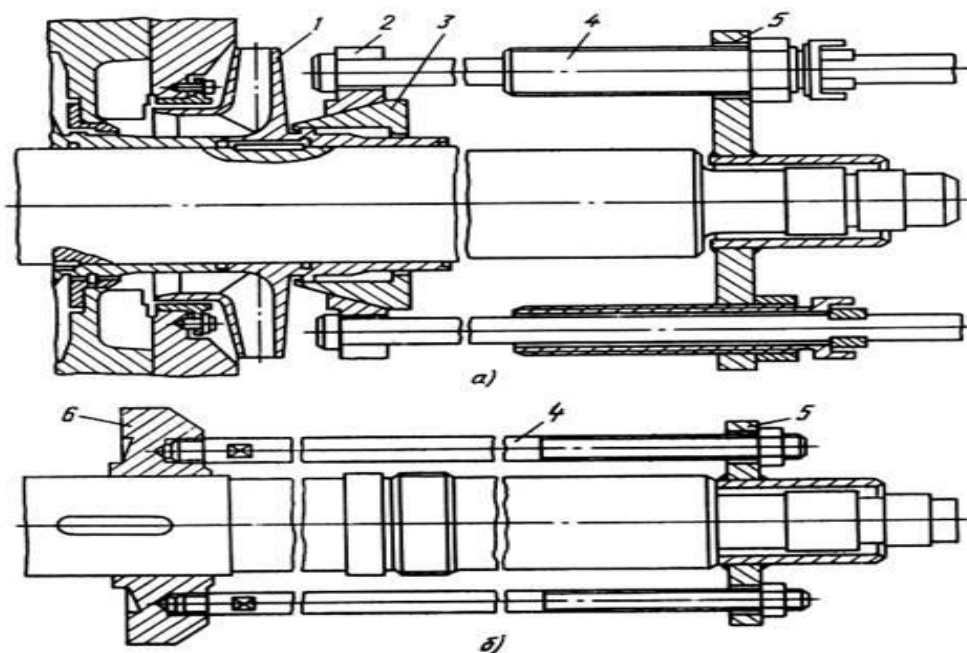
Приспособления для снятия деталей с вала насоса
